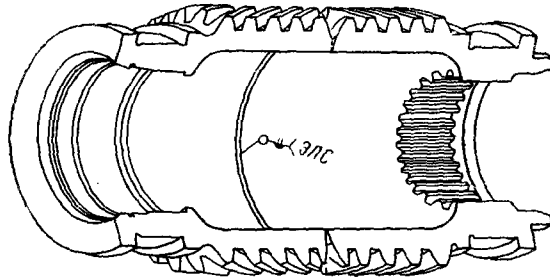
Шестерни, соединенные электроннолучевой сваркой
